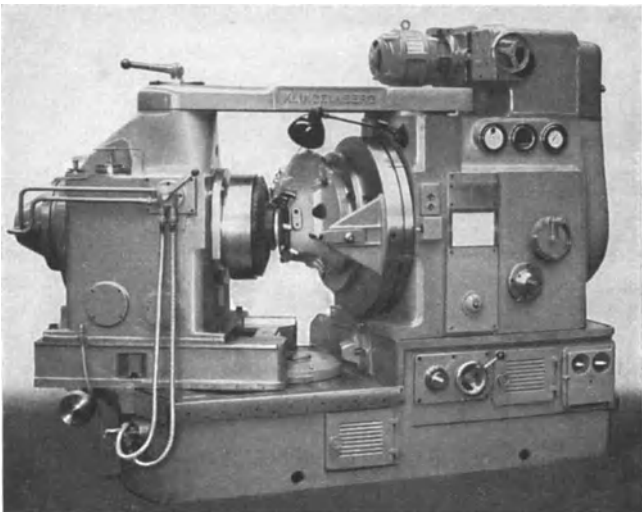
Selbsttätige Walzfrasmachine für Klingelnberg-Palloid-Spiralkegelräder.
